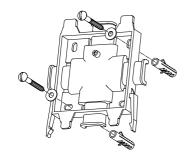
Wand-/Rohrhalterung mit Unterlegscheiben anschrauben
